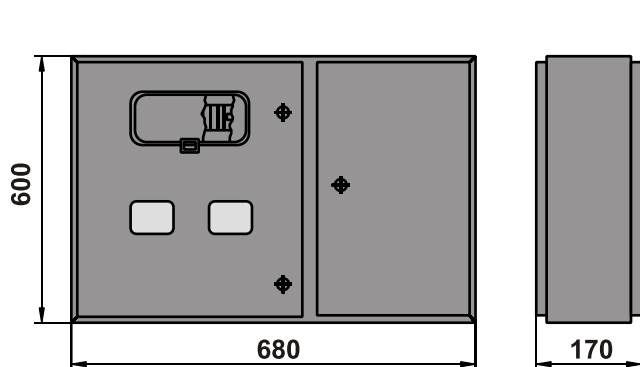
Внешний вид и габаритные размеры ЩЭЗО-2100Н
